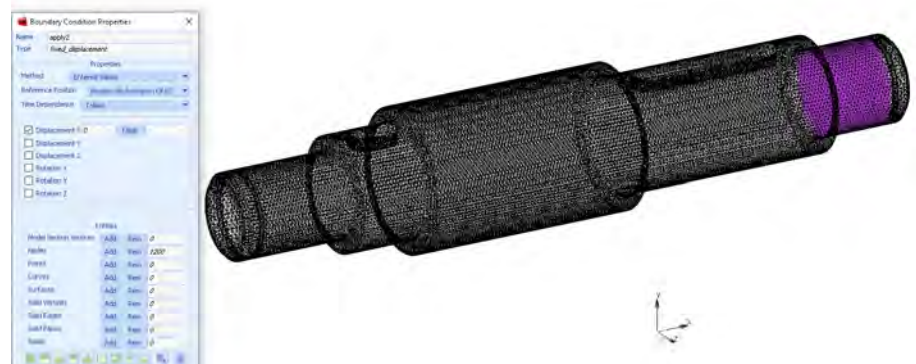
Detalle de la fijación en el apoyo B del eje intermedio
